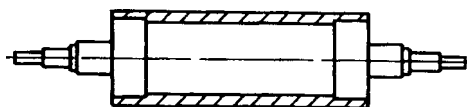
Формный цилиндр с приваренными цапфами.
